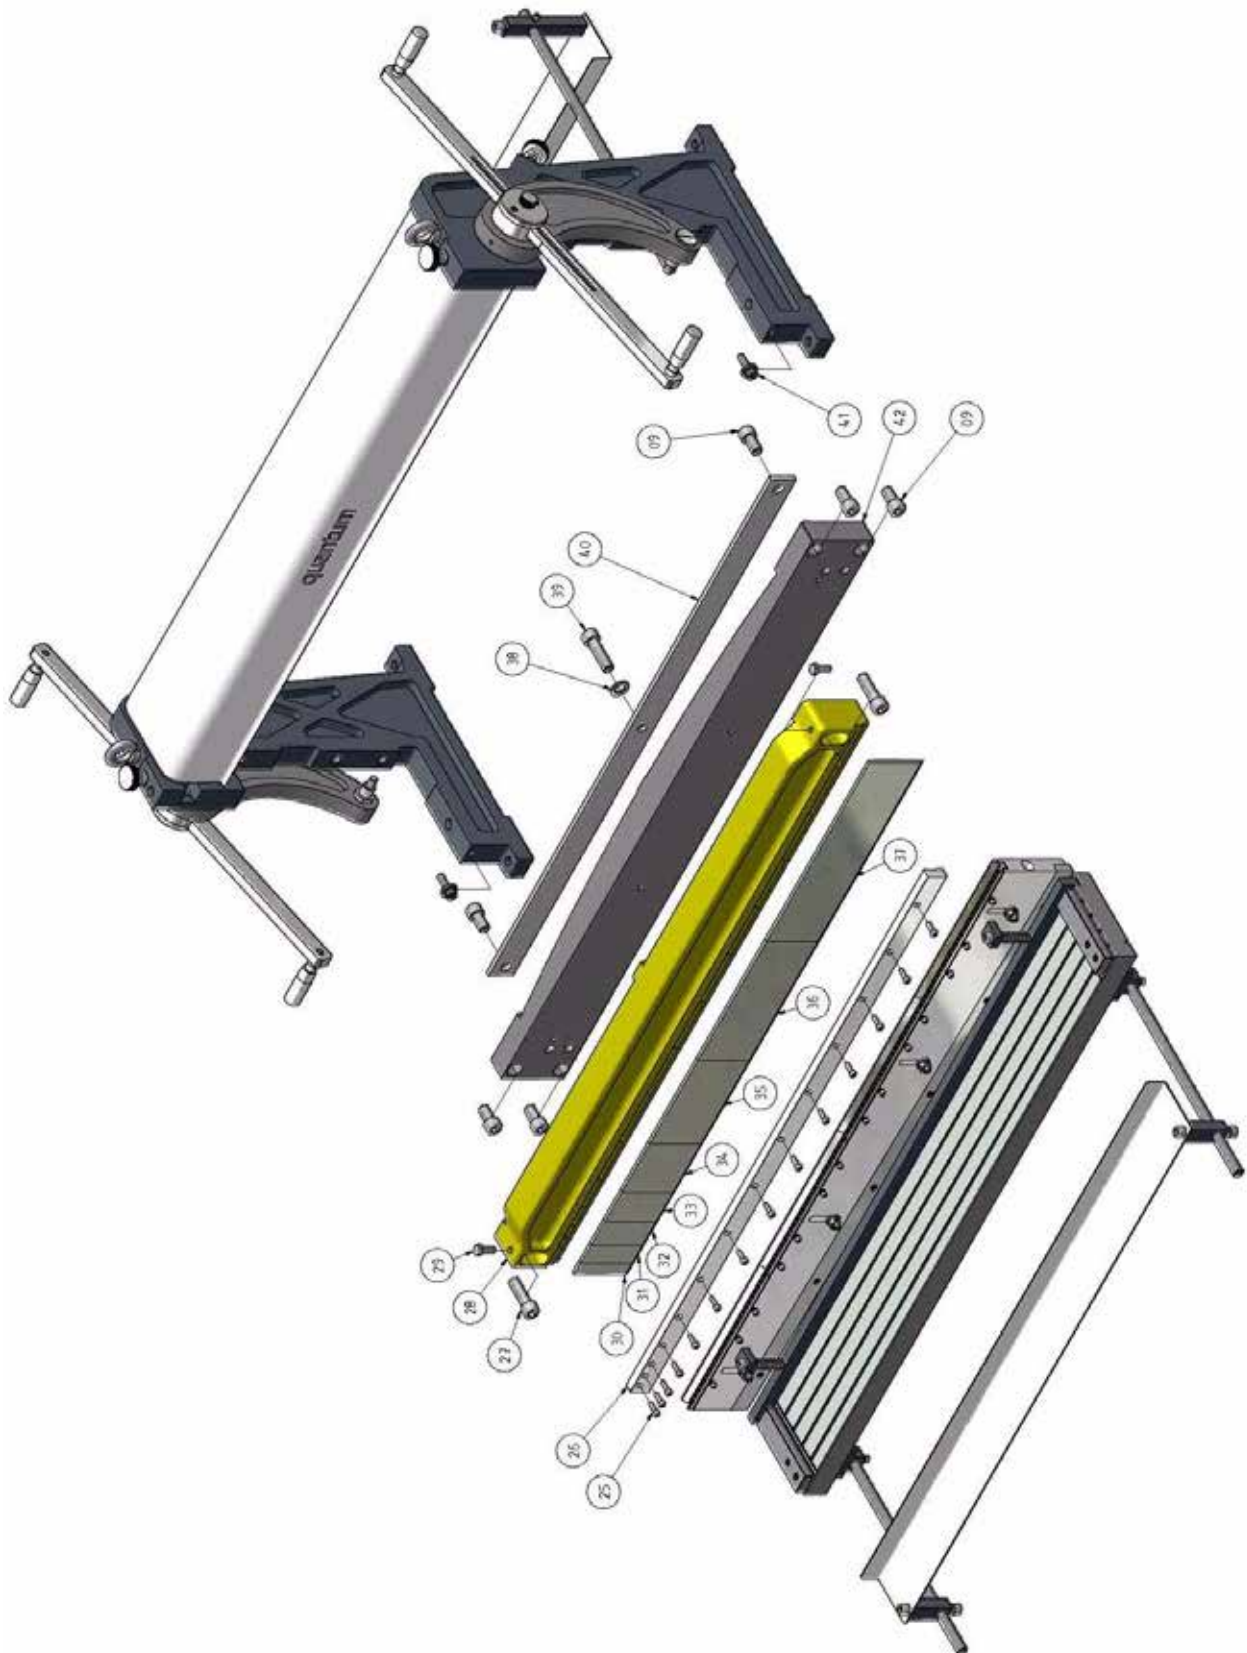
Ersatzteilzeichnung 2-4 - Drawing spare parts 2-4
